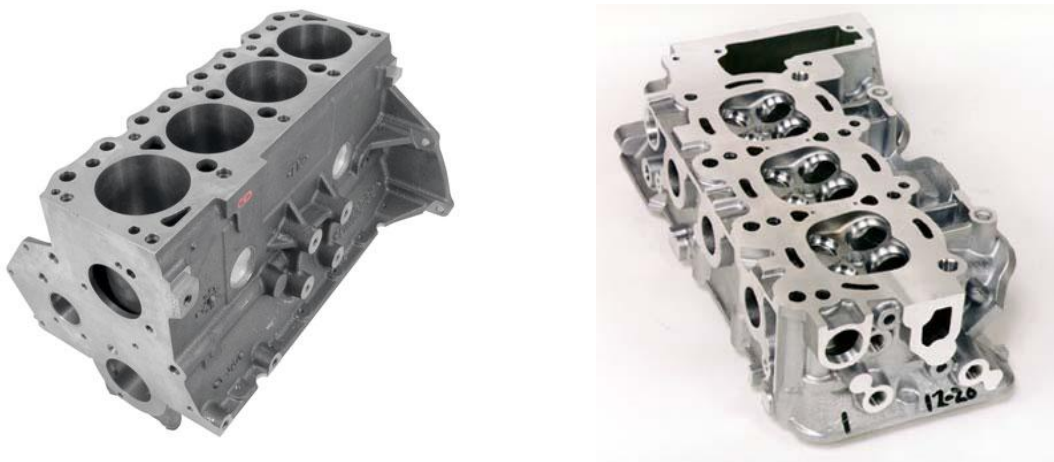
Bloco do motor (à esquerda) e cabeça do motor (à direita) [19] [20]
